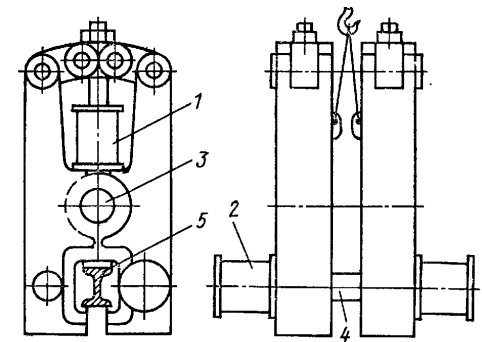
Схема подвесной сварочной головки для сварки стыков рельсов в пути
